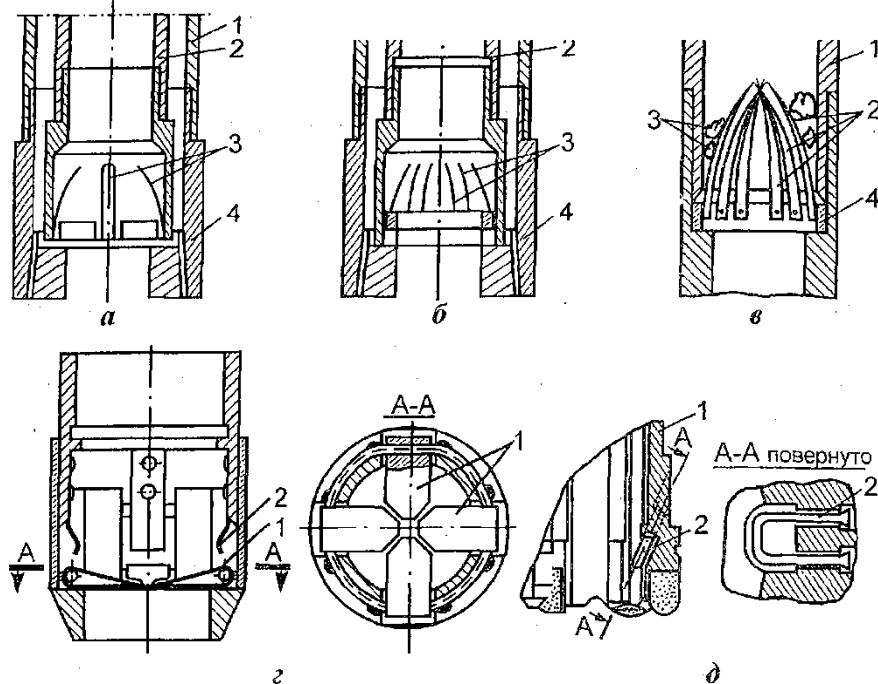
Схемы кернорвательных устройств, применяемых в колонковом бурении: а, б- пластинчатого или проволочного типа: 1- наружная колонковая труба; 2- керноприемная труба; 3- стальные кернозахватывающие элементы; 4~ коронка; в - схема выхода из строя пружинных кернозахватывающих пластинок: 1 - колонковая труба; 2 - кернозахватывающие элементы; 3 - кусочки породы; корпус кернозахватывающего устройства; г - кернорвательное устройство рычажкового типа: 1 - рычажки; 2 - пластинчатые пружины; д~ кернорвательное устройство заклинивающего действия: 1 - коронка; 2 - скоба
